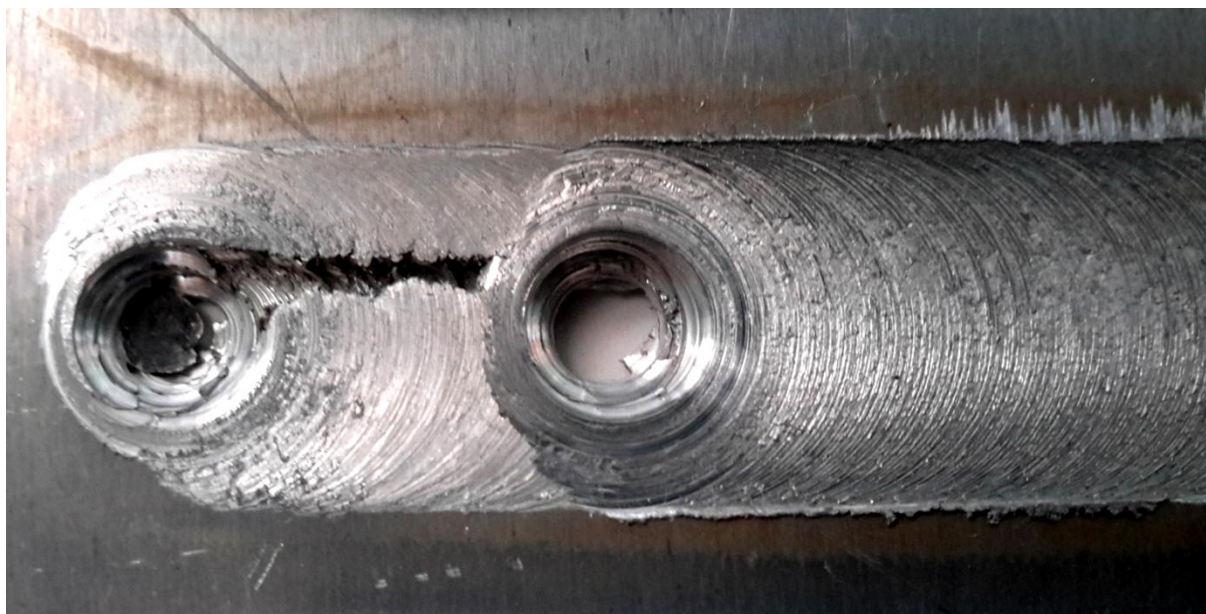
Подварка вторым проходом дефектов типа несплавления, дефект типа wormhole и несплавления в корневой части шва:
